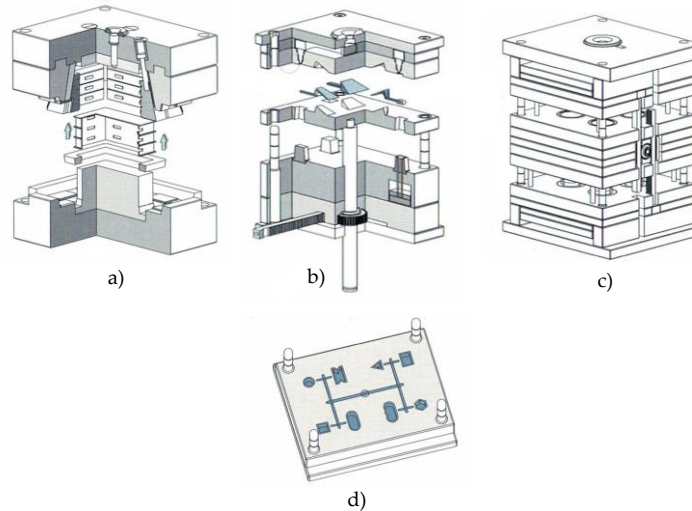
Outros moldes: a) *Split Molde*; b) Molde Bi-material; c) Molde *sandwich*; d) Molde família (adaptado de Centimfe, 2003)
